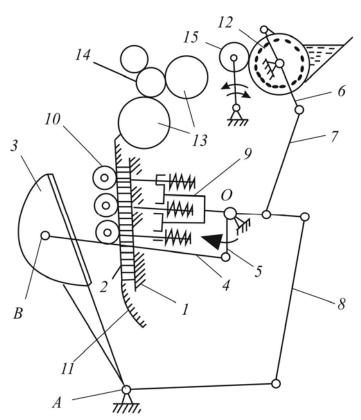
Кинематическая схема тигельной машины легкого типа: 1 — талер; 2 — форма; 3 — тигель; 4 — шатун; 5 — кривошип; 6—8 — рычаги; 9 — каретка; 10 — накатные валики; 11 — направляющие; 12 — дукторный цилиндр; 13 — раскатные цилиндры; 14 — раскатной валик; 15 — передаточный валик
